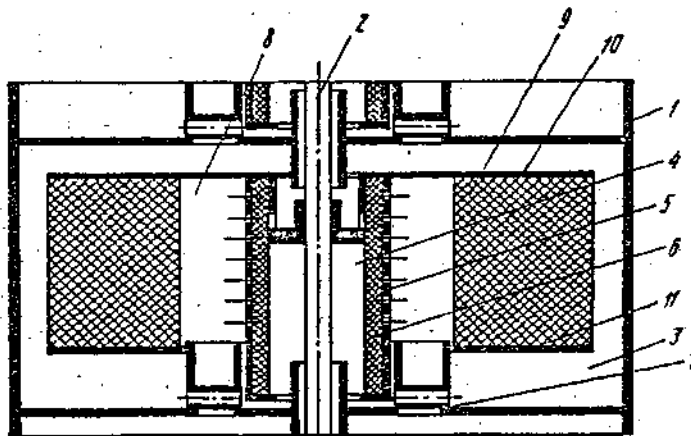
Роторный теплообменный аппарат: 1 – корпус; 2 – вал; 3 – контактная ступень; 4 – распылительный ротор; 5 – перфорированный цилиндр; 6 – заборное устройство; 7 – переливное устройство; 8 – перераспределительный элемент; 9 – кольцевая насадка; 10 – верхний диск; 11 – нижний диск.
